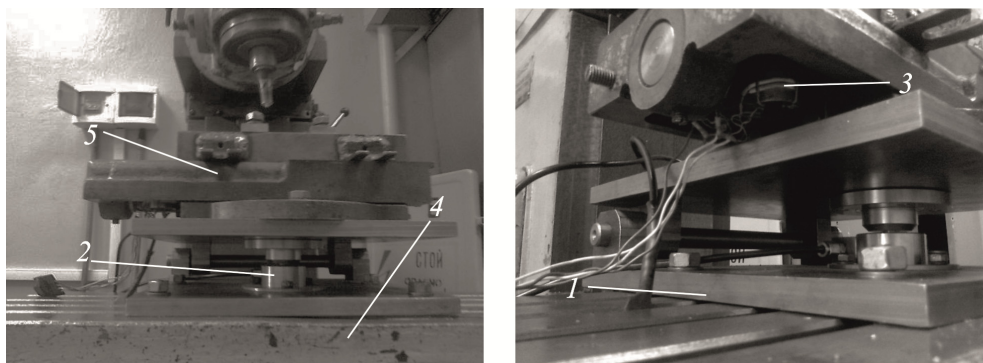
Приспособление для измерения осевых и продольных усилий: 1 – крепежная плита; приспособление для измерения осевого усилия; 2 – датчик осевого усилия; 3 – датчик продольного усилия; 4 – стол фрезерного станка; 5 – салазки суппорта токарного станка
